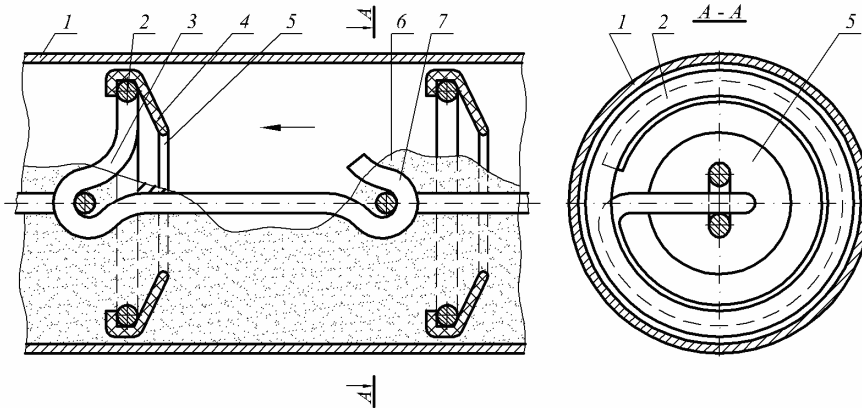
Конструктивна схема робочого органу скребкового транспортера-змішувача
